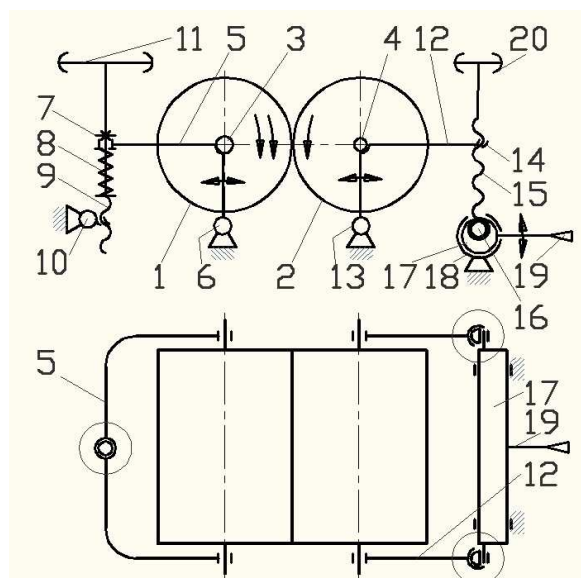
Конструкция установочного механизма с регулировкой двух вальцов
